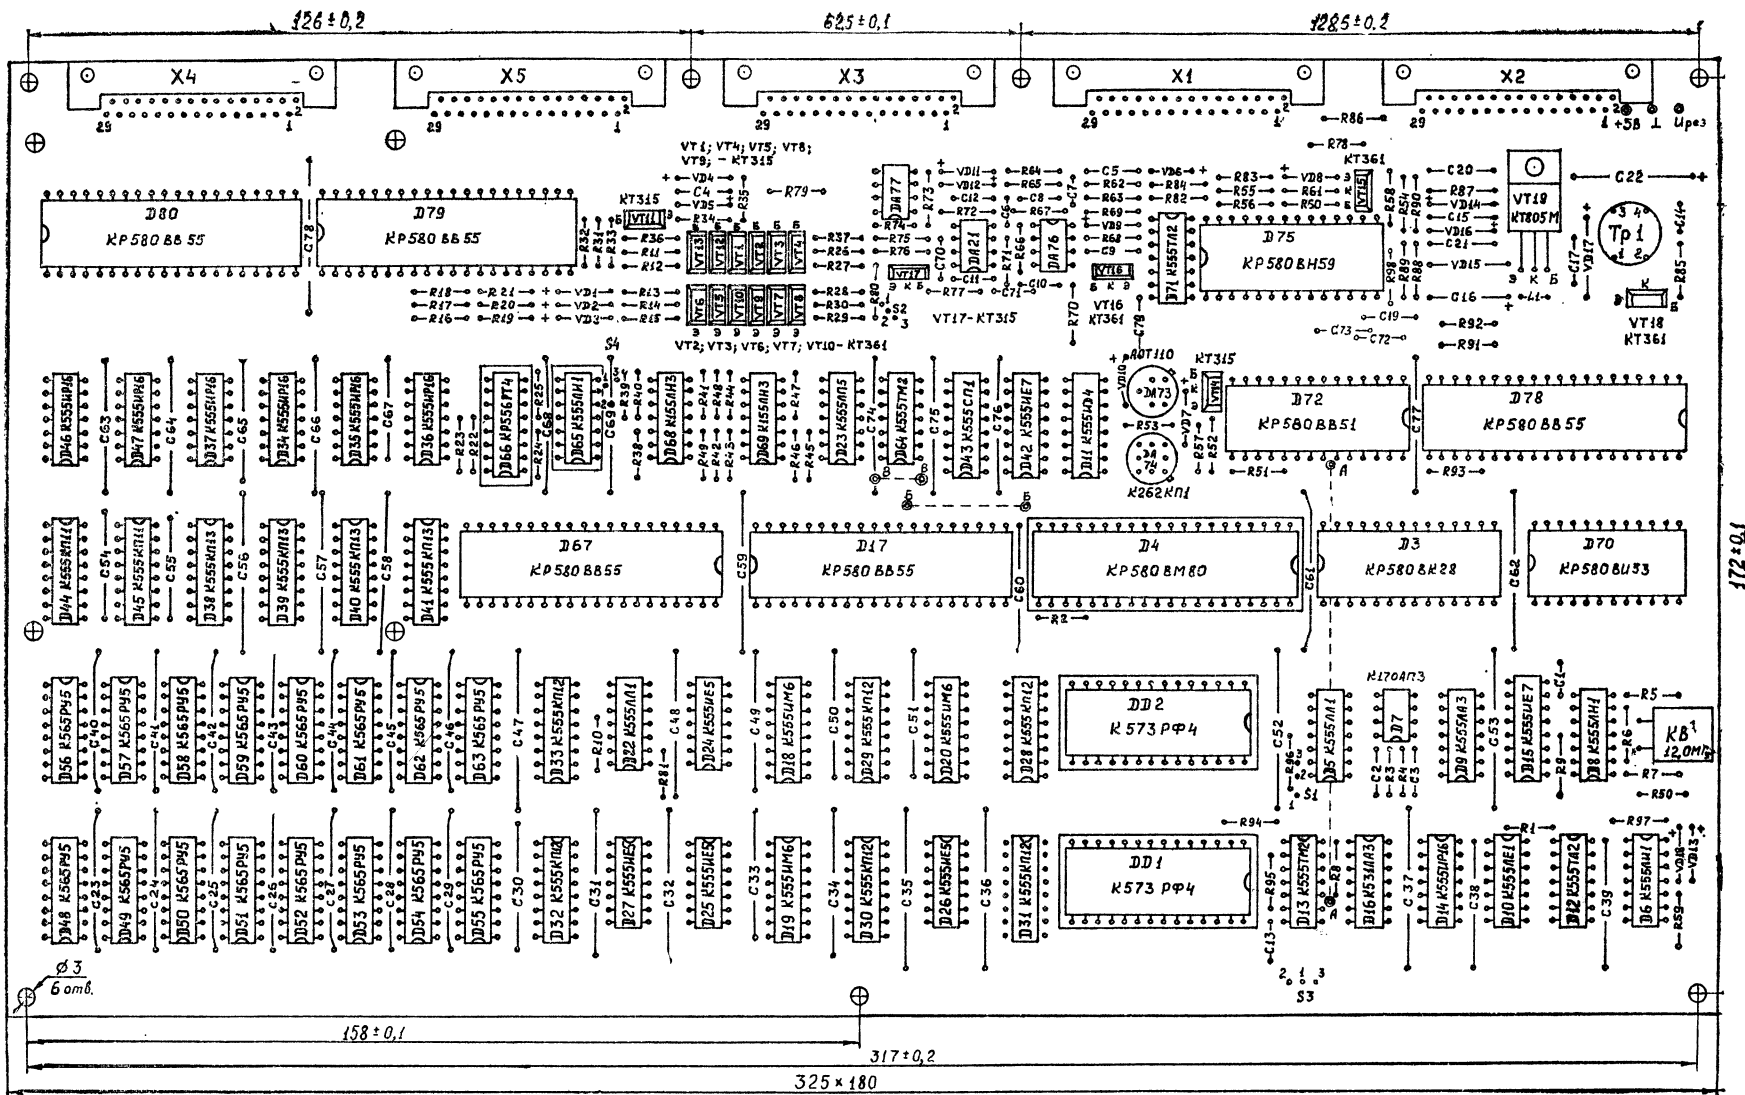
Сборочный чертеж печатной платы ПЭВМ
